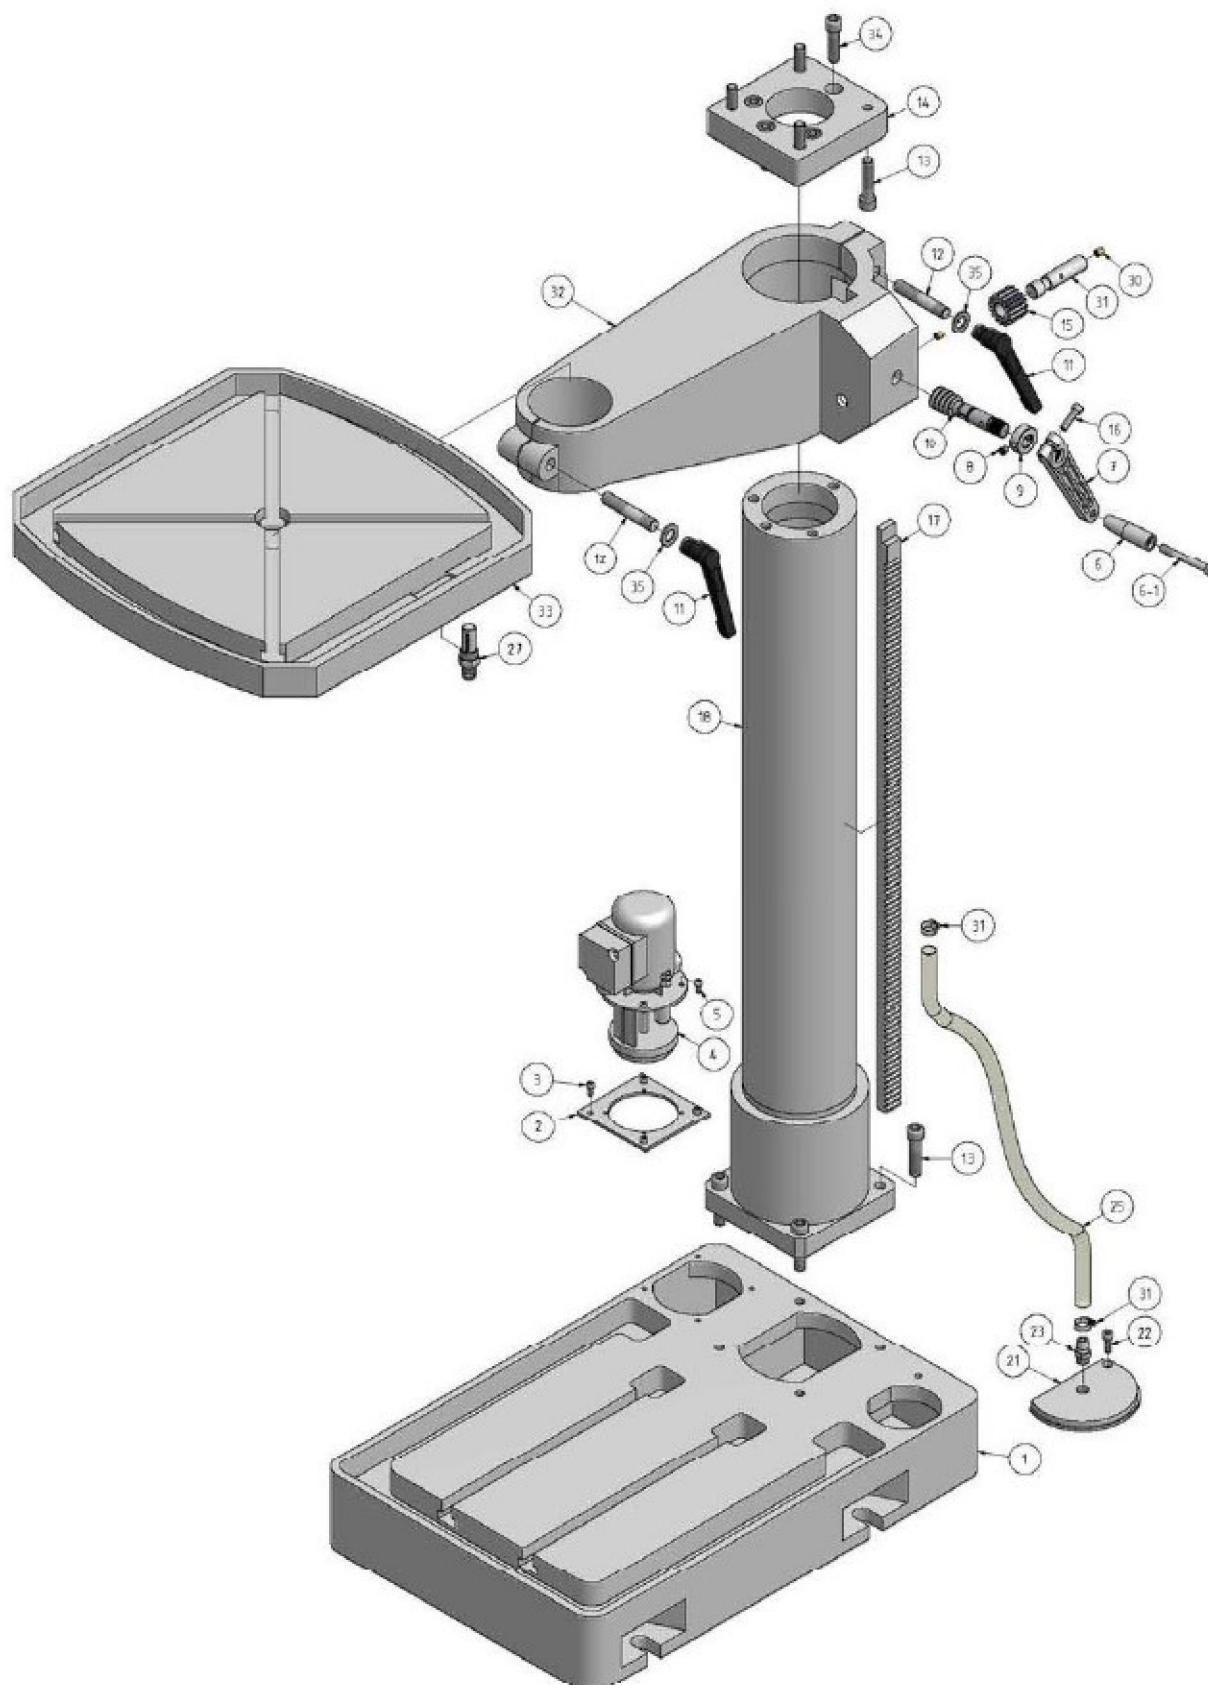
Columna y mesa de perforación - Column and drilling table
